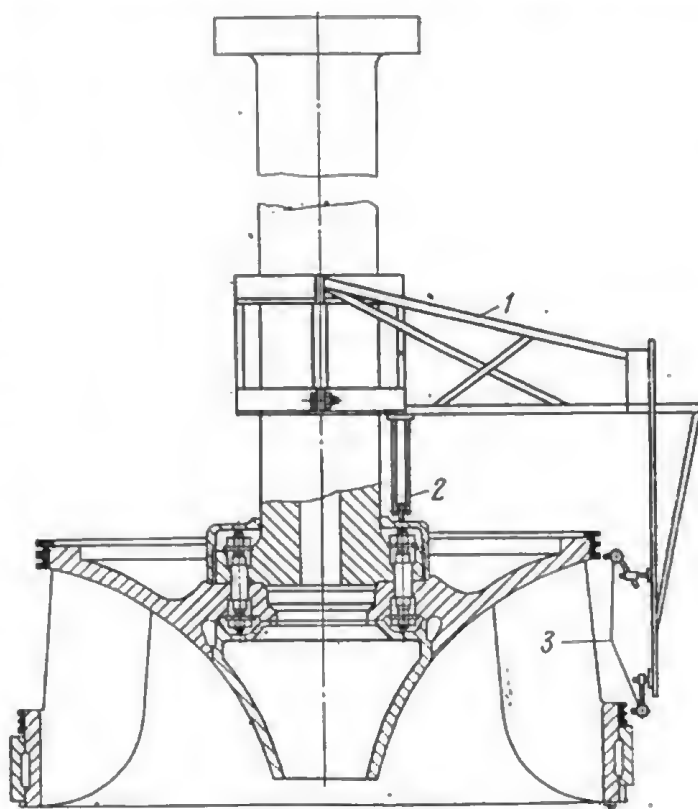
Приспособление для проверки concentричности лабиринтных колец.
